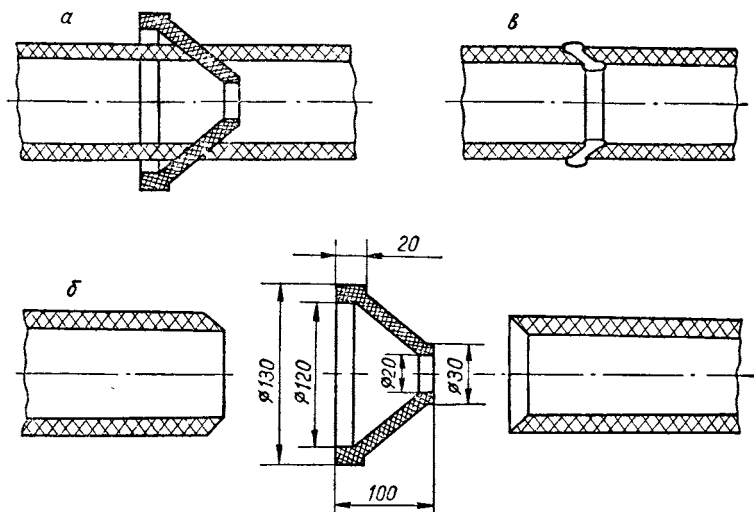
Последовательность процесса раструбно-стыковой сварки:
